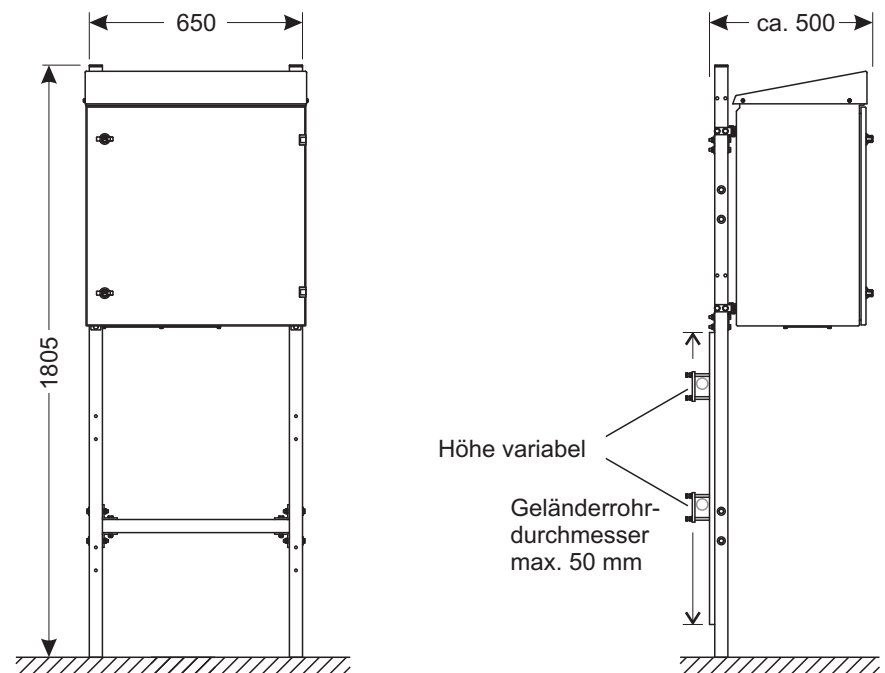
Maßzeichnung P 700 IQ Montage an einem Geländer (Maße in mm)
